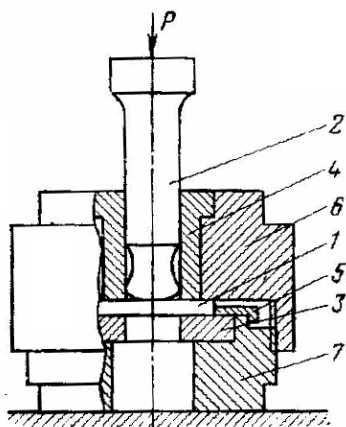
Приспособление для испытания на срез листа по круговому контуру:
